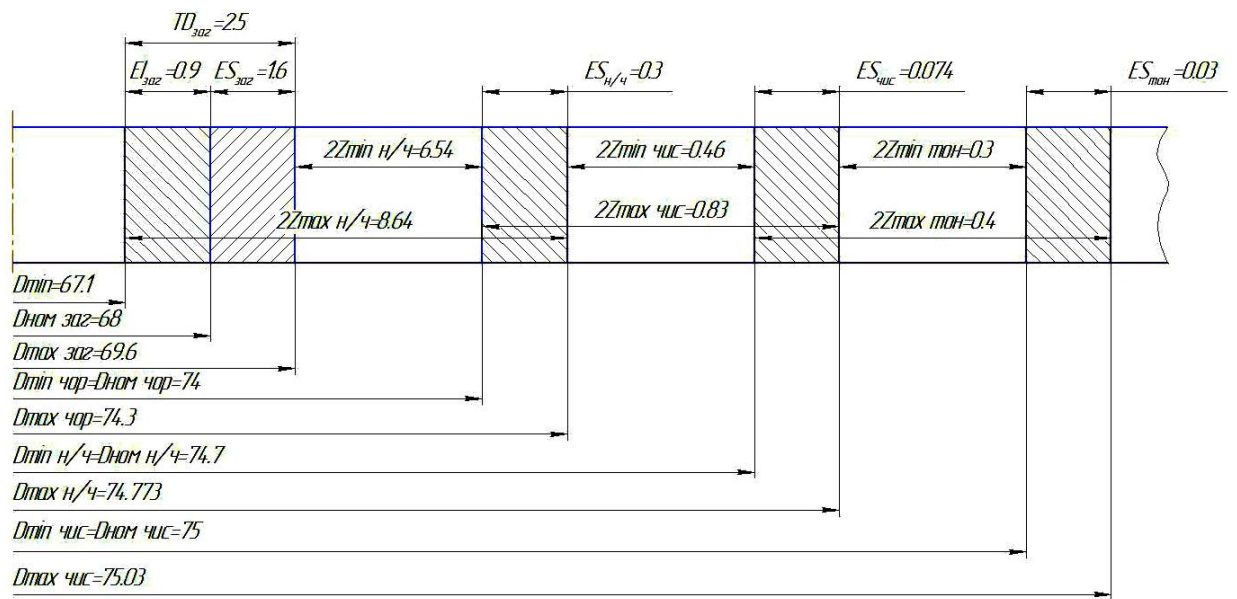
Схема розташування допусків і припусків при обробці розміра $\varnothing 75(+0,030)$ втулки зубчастої
